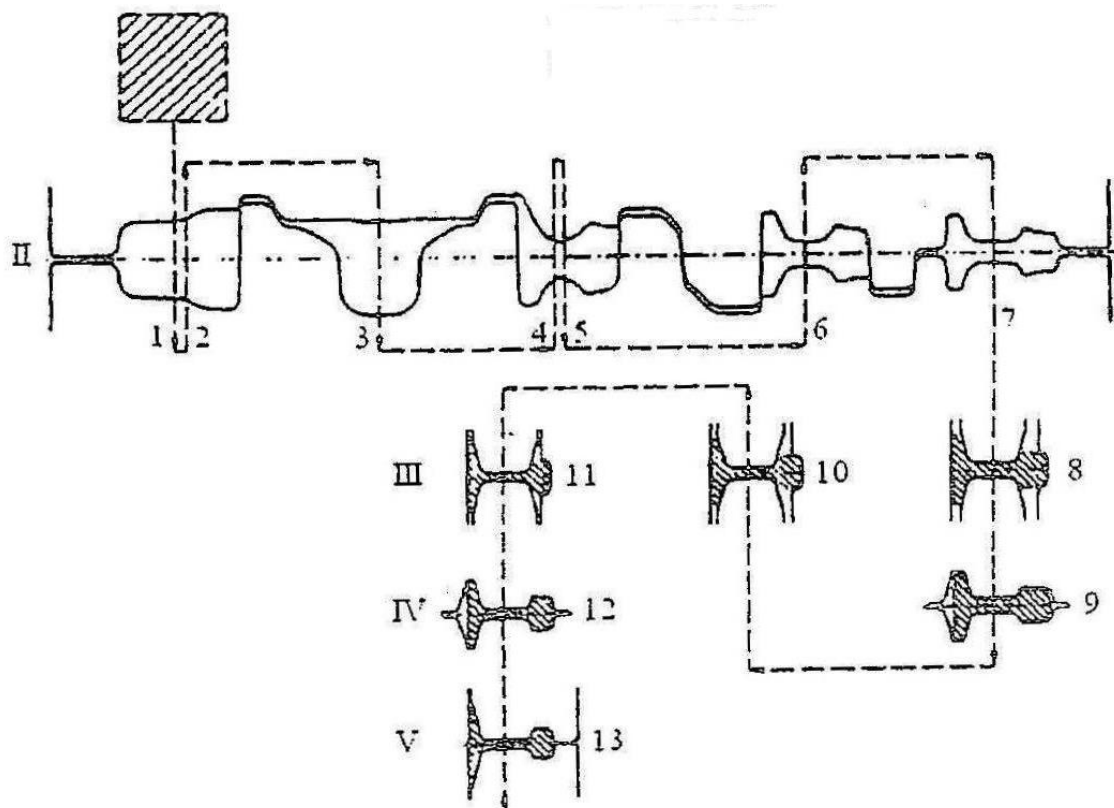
Типовая схема калибровки для прокатки рельсов фирмы SMS [1]
